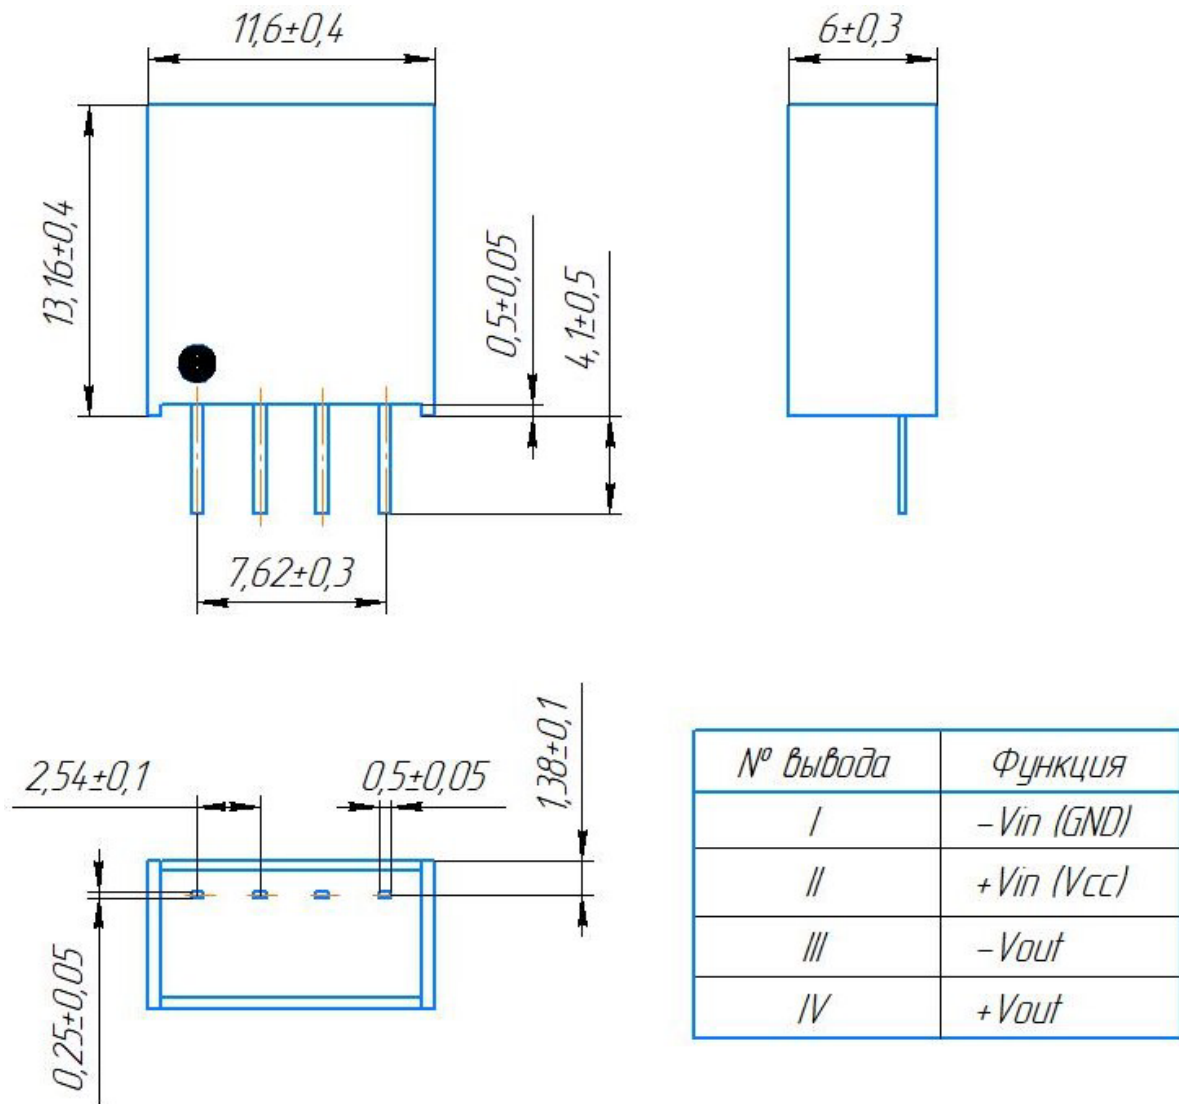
Габаритный чертеж и назначение выводов преобразователя DC-DC ZVR1.5-0515
